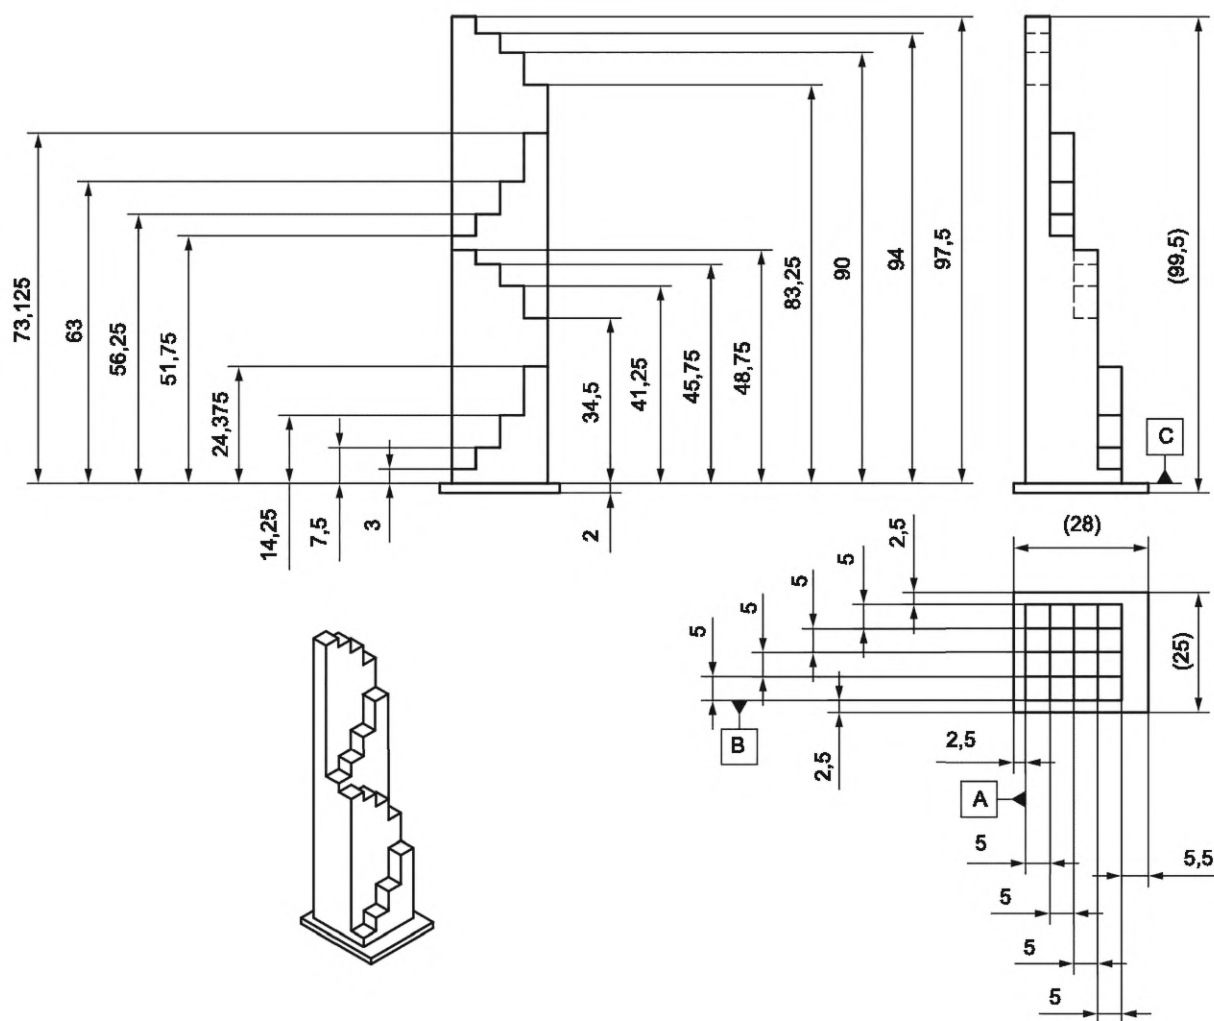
Общий вид среднего ступенчатого образца для испытаний
